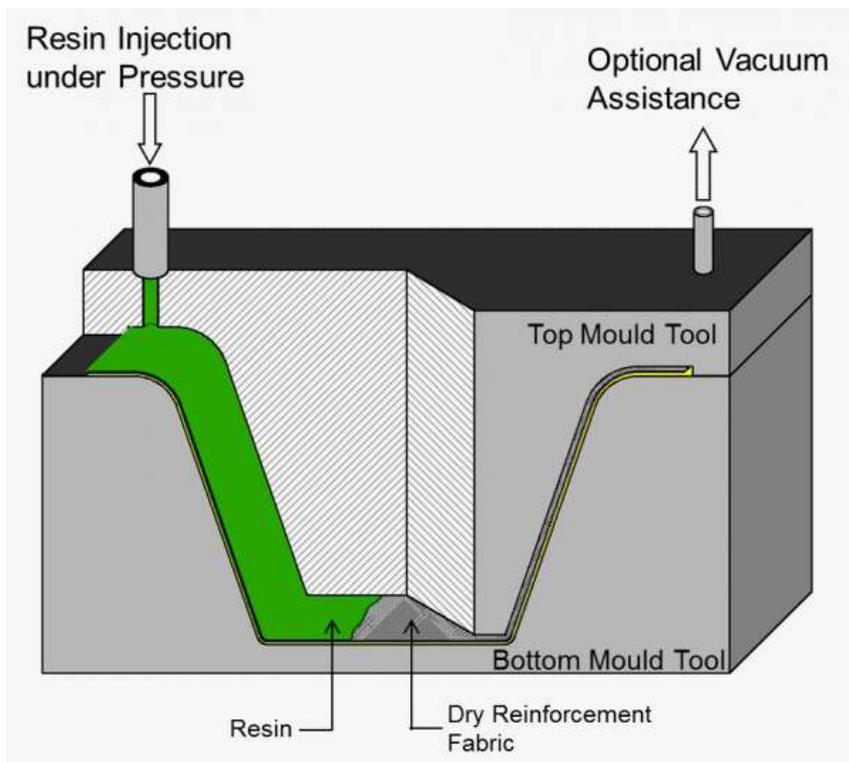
Exemplo de tecnologia RTM (Resin Transfer Molding)
